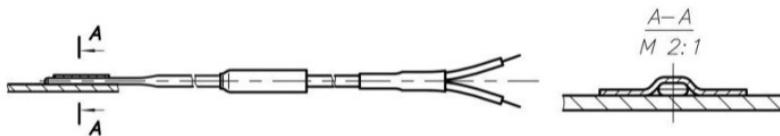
Способ монтажа датчика на основе КТМС на плоскую поверхность с помощью сварки
